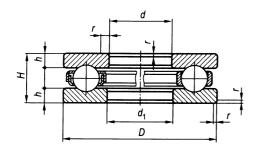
Подшипник шариковый упорный одинарный размерных серий 1008000 и 8000H ($d_1 \ge d+2$)
